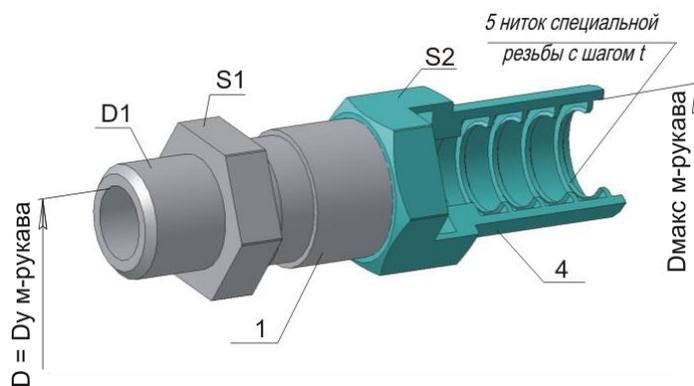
Конструкция кабельного ввода для монтажа кабеля в металлорукаве
